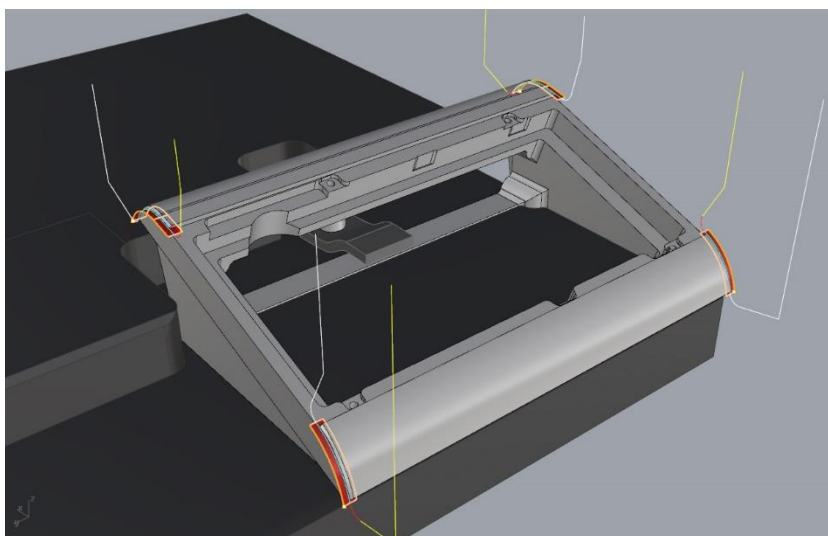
Druhé upnutí – dokončování fréza 4 mm – Standard Drill
